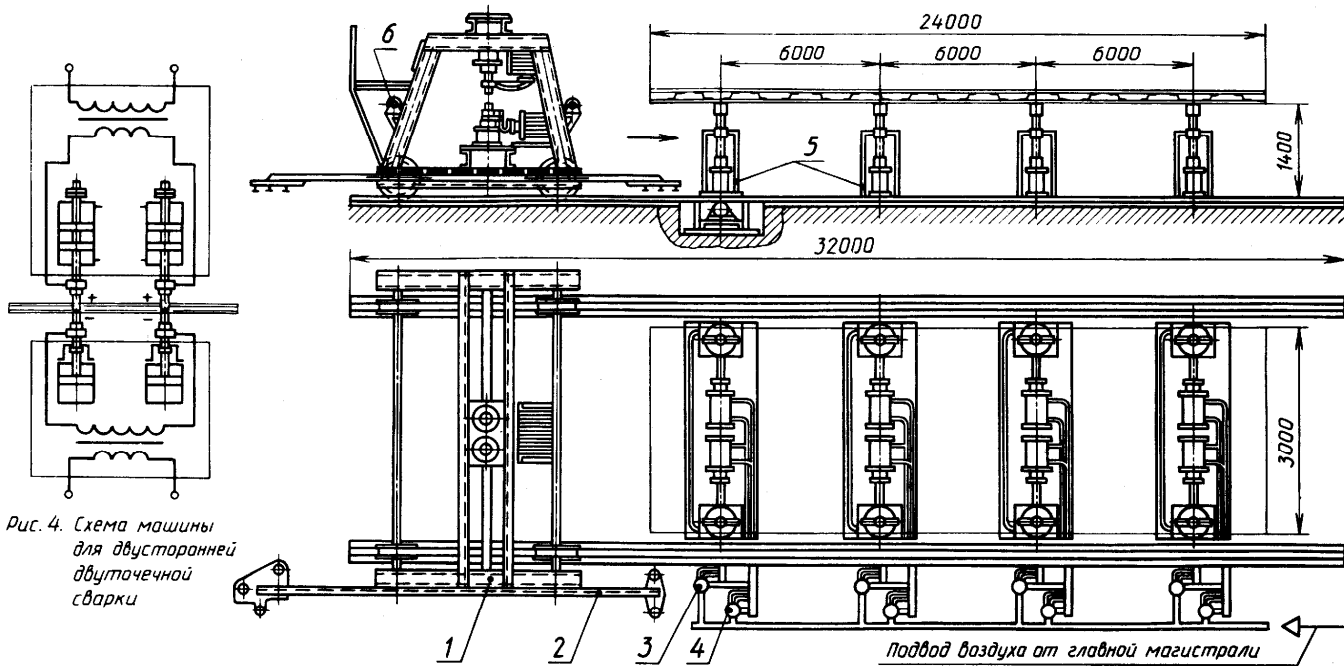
Схема машины для двусторонней дугочечной сварки
